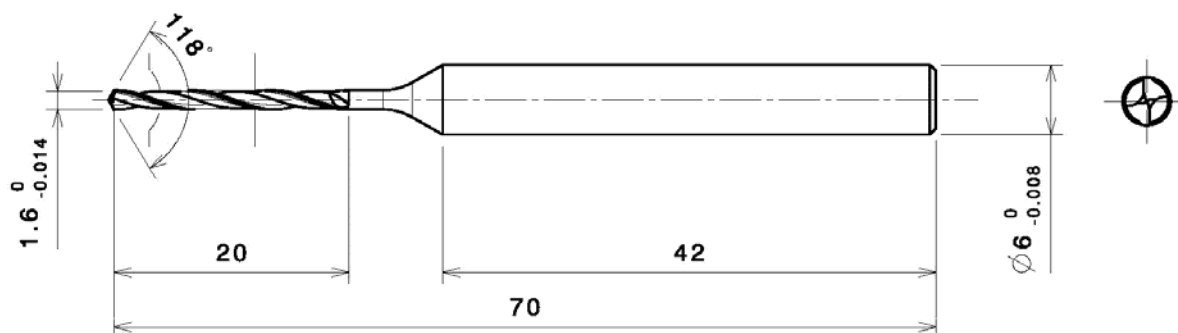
Чертеж твердосплавной фрезы SSD D1.6X20FX 70-6 из сплава UF10
